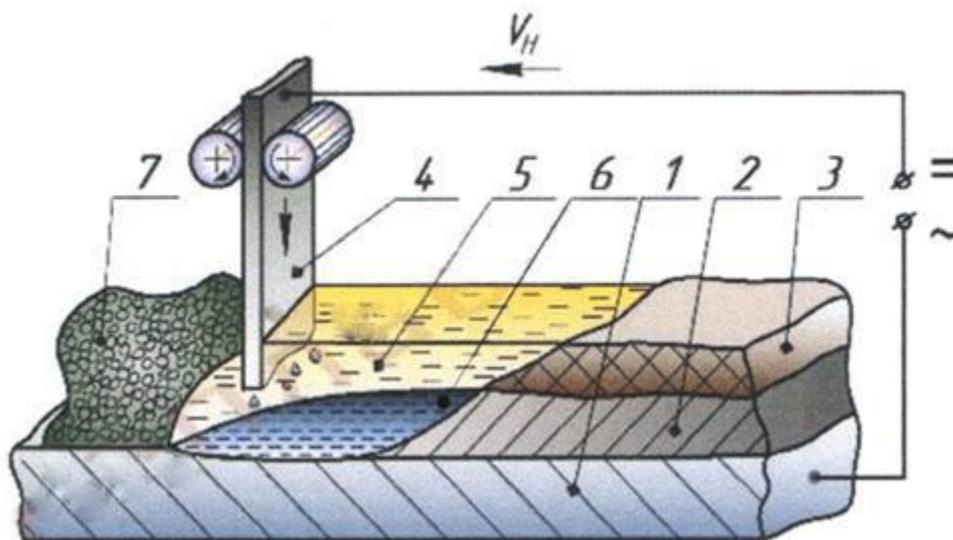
Схема процесса электрошлаковой наплавки: 1 – основной металл; 2 – наплавленный металл; 3 – шлаковая корка; 4 – полоса наплавляемого металла; 5- шлаковая ванна; 6 – кристаллизатор; 7 – сварочный флюс
